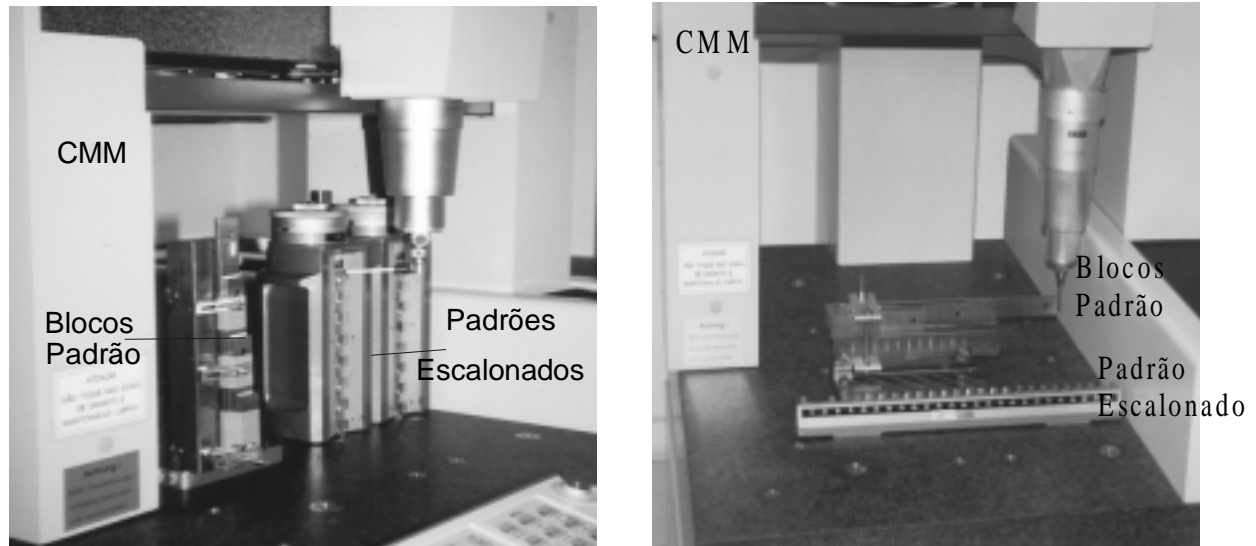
Calibração de padrões escalonados (com tambor micrométrico e horizontal) utilizando CMM e blocos padrão
